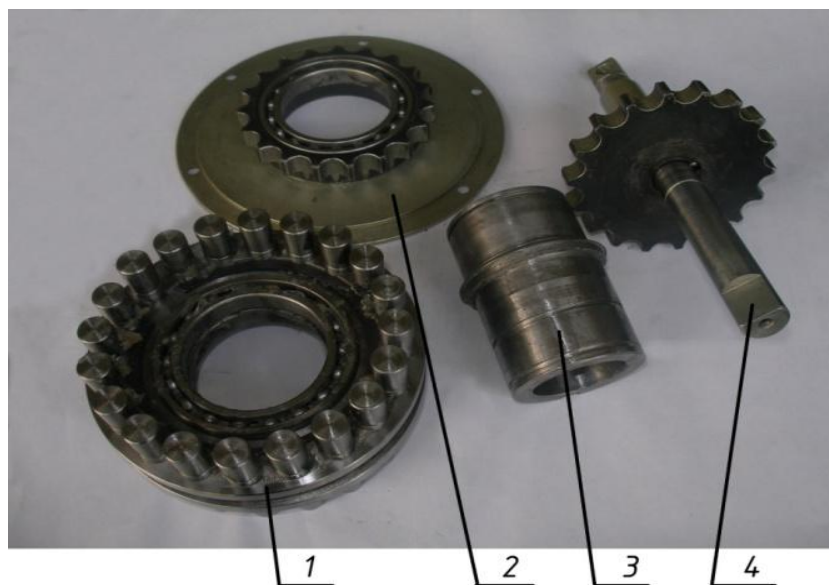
Вид основных деталей прецессионного редуцирующего механизма лебедки после проведения эксплуатационных испытаний: 1 – сепаратор с роликами; 2 – звездочка подвижная; 3 – косо́й вал; 4 – звездочка неподвижная с основным валом
